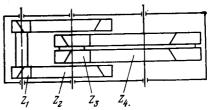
Кинематическая схема редуктора Ц2НШ-750Б
